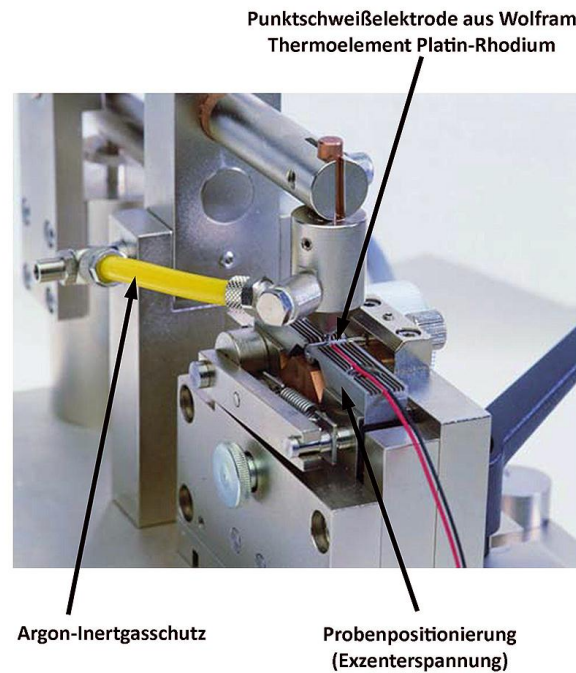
Aufschweißen des Platin-Rhodium Thermoelementes auf die Probe.
